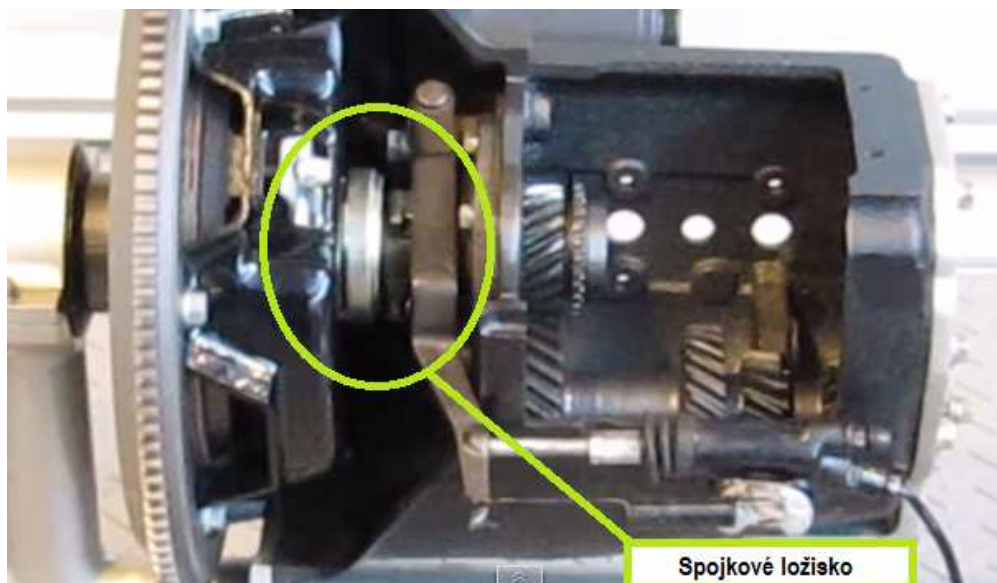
Spojkové ložisko ako súčasť systému [18]
